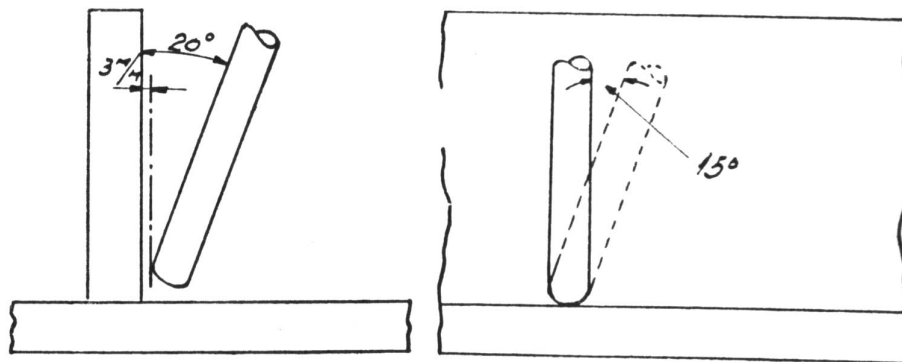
Solda na posição horizontal (Buzzoni, 1962)
